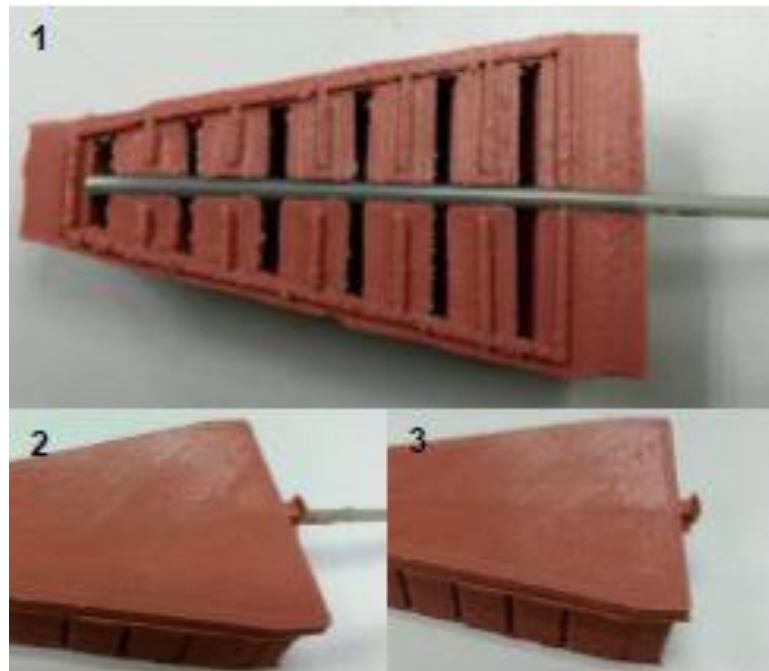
1) Protección cámaras 2) Ensamblaje 3) Dedo completado
